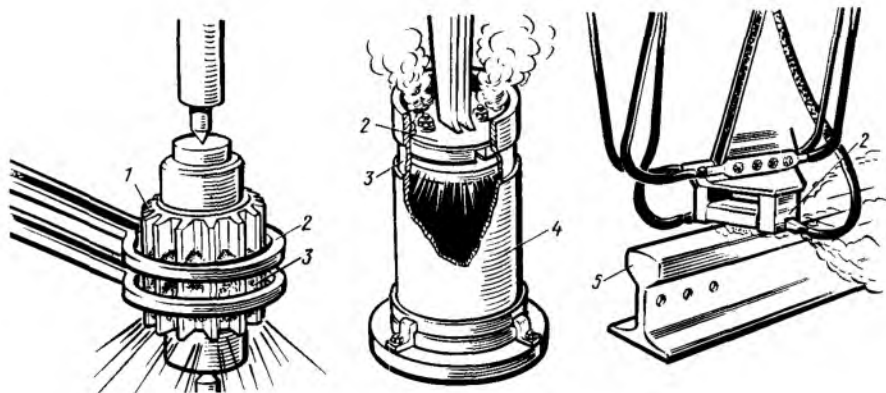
Закалка металлических изделий с помощью вихревых токов:
